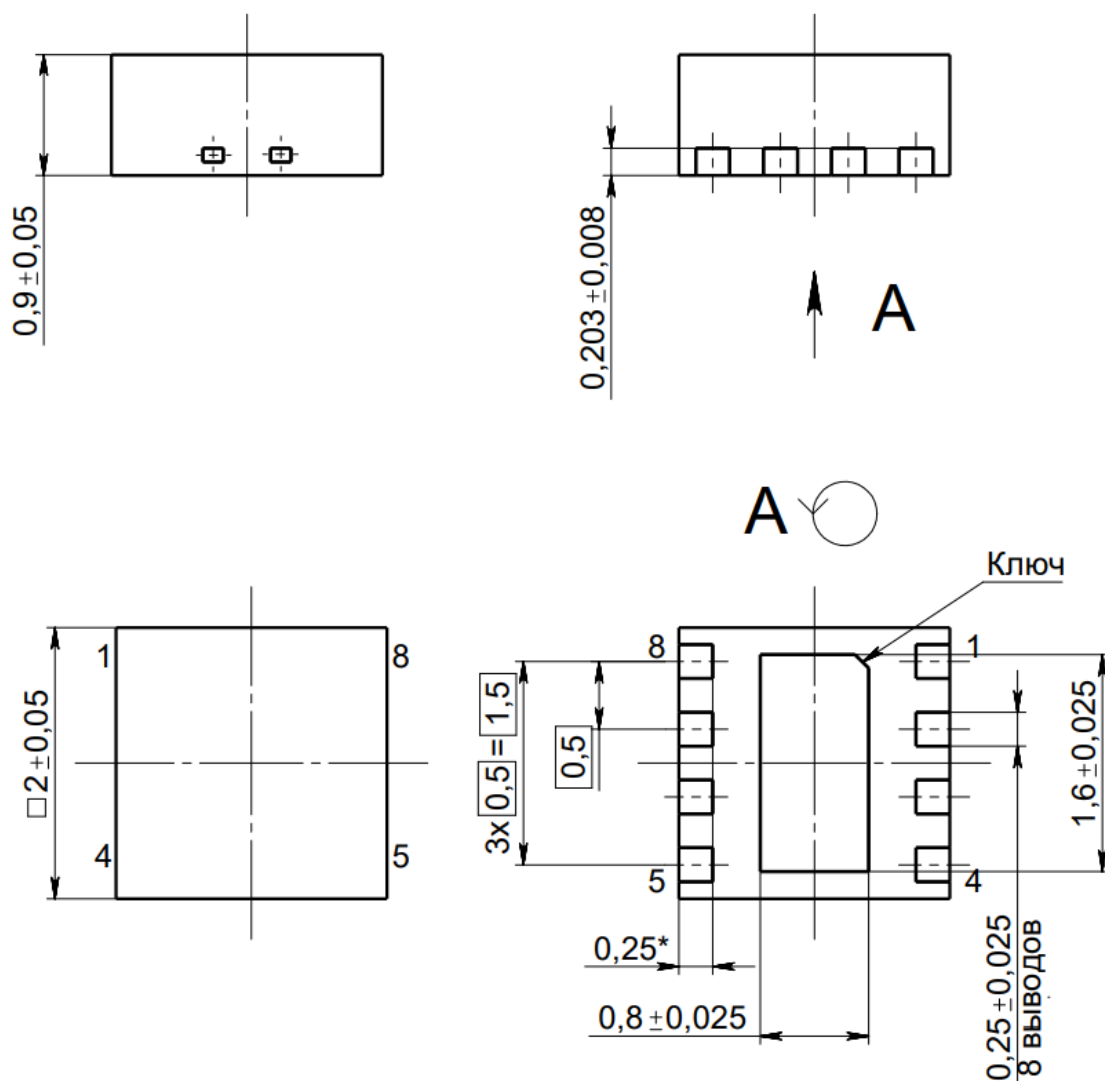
Габаритный чертеж корпуса 5239.8-1 К (размеры в мм)
